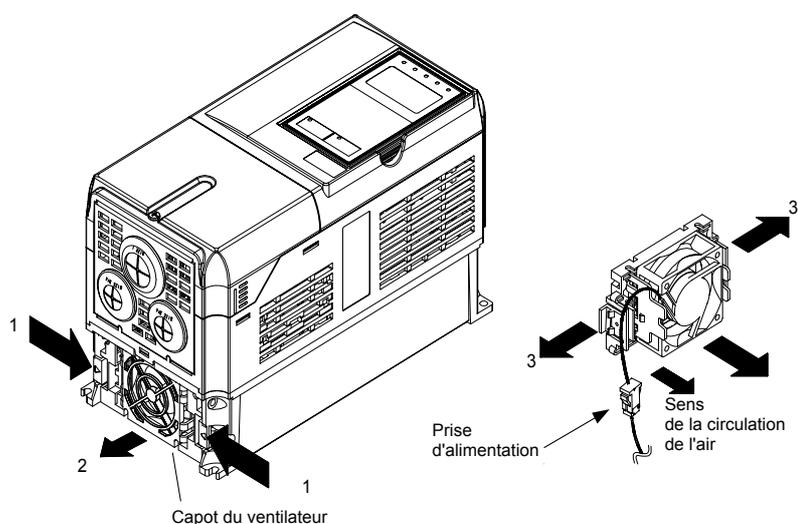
Remplacement du ventilateur (variateurs de 18,5 kW ou moins)
